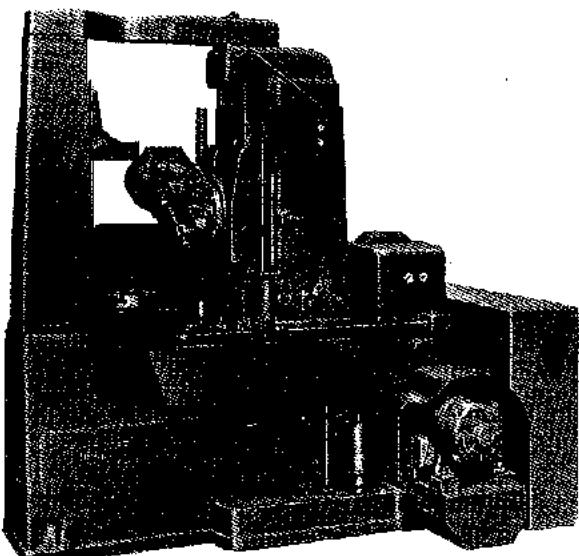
Máquina especial para tallar engranajes con fresa-madre (Gould & Eberhardt, Inc.)
